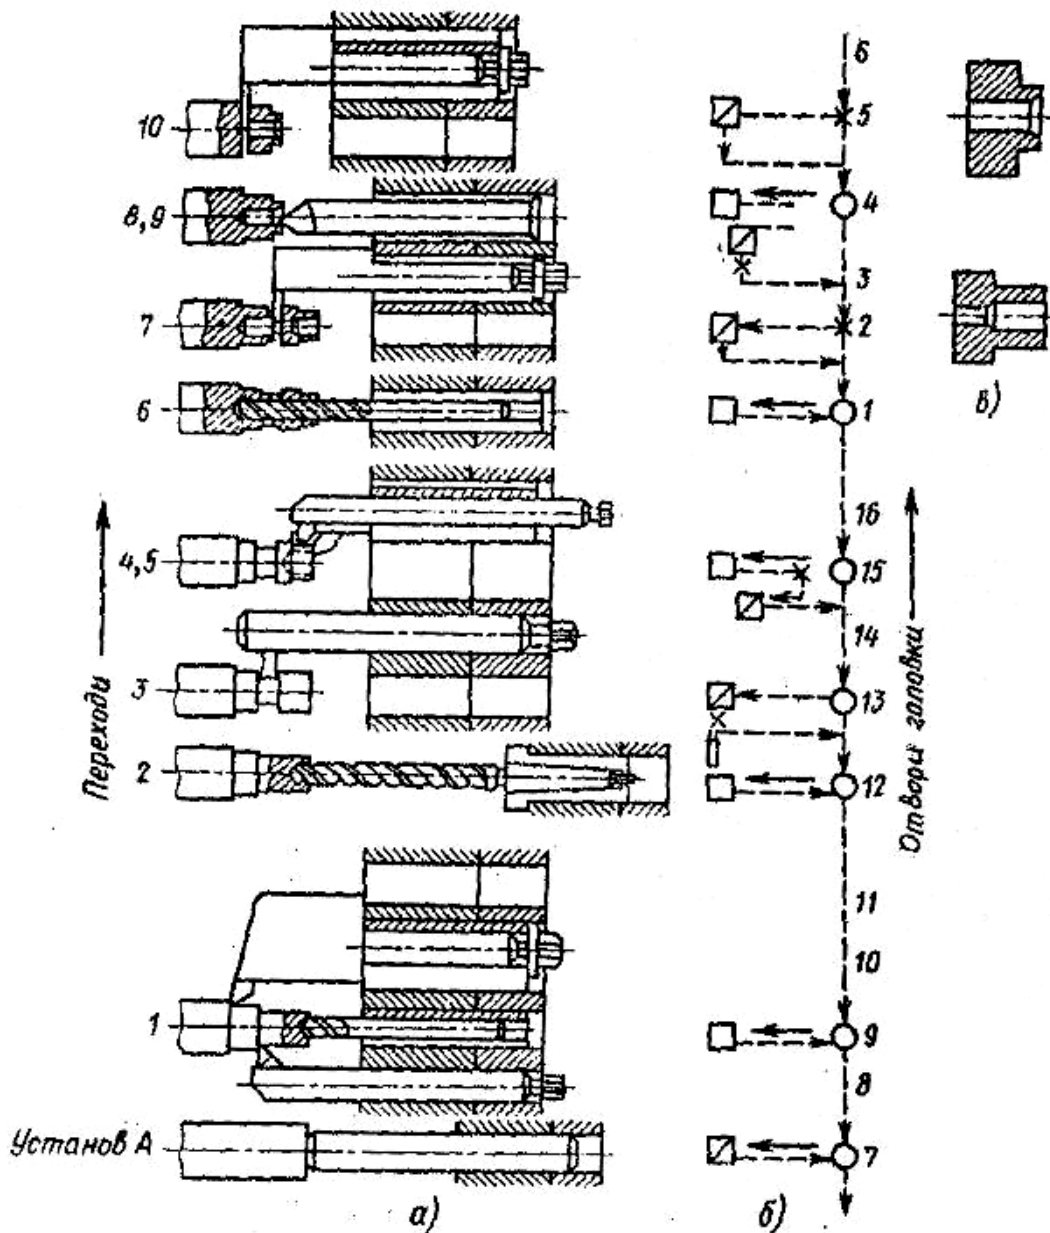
Схема налагодження токарно-револьверного верстату моделі 1К341
